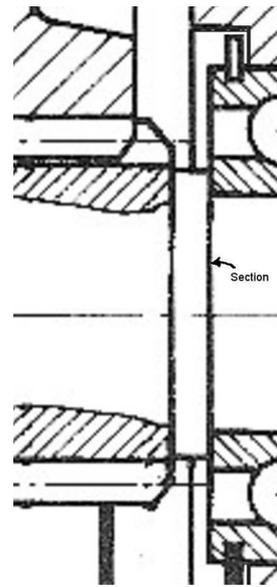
Zoom sur la section épaulée (échelle 1 : 1).
